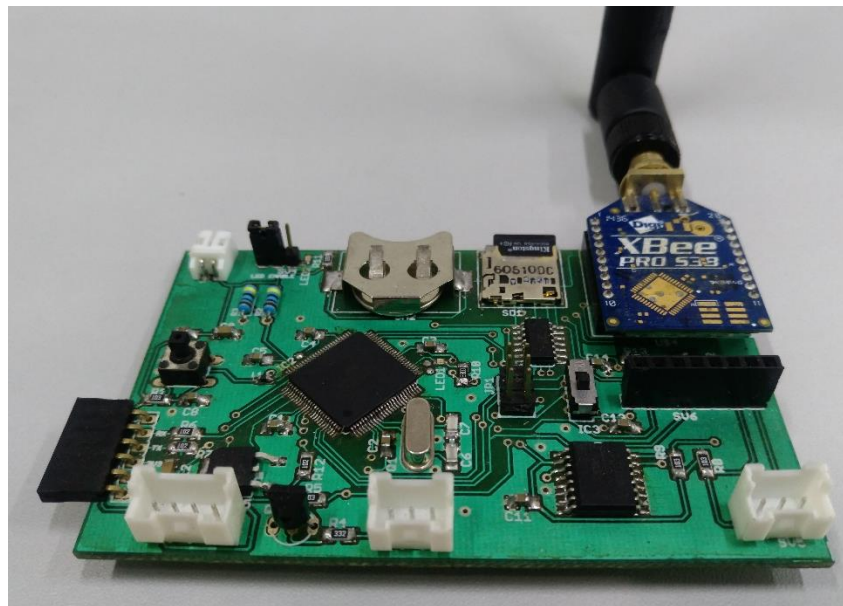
PCB con montaje de radio XBee-PRO 900HP
